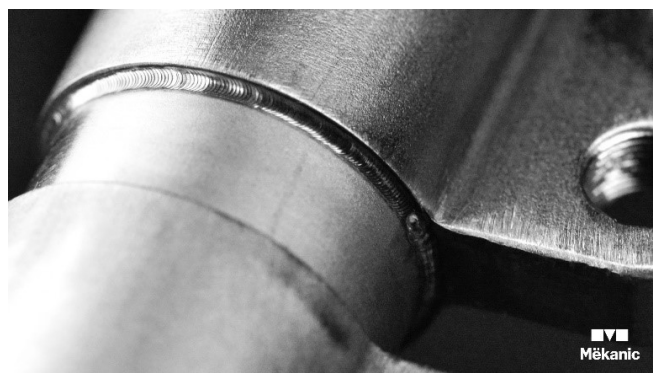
Zoom sur la soudure au laser entre le canon et son tube ©2020 par Mëkanic.
